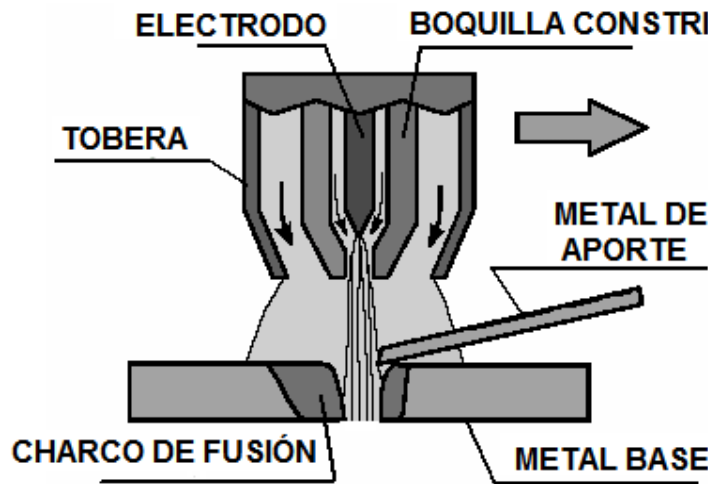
Esquema del proceso de soldadura por arco de plasma (3, 18)
